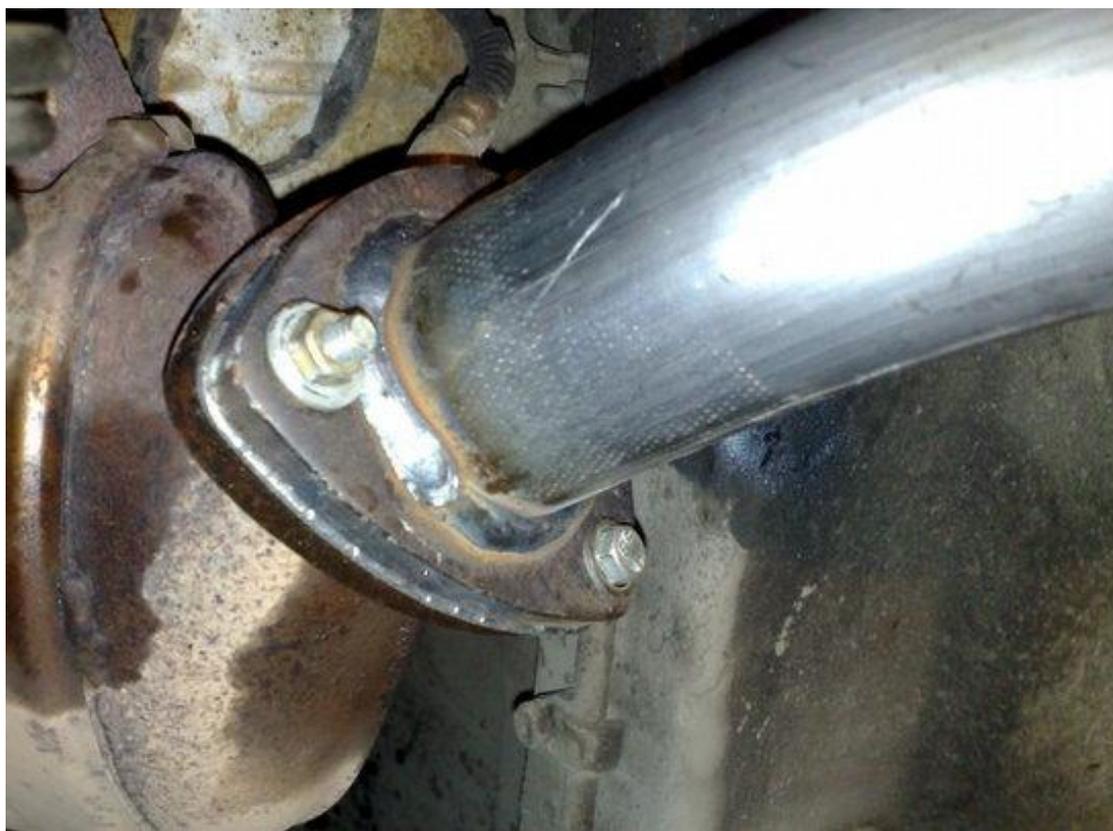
Гайки крепления резонатора к катализатору.
